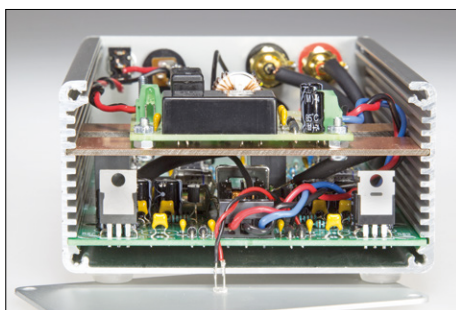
Die Platine der Stromversorgung und die Vorverstärkerplatine sind in das Gehäuse eingeschoben.
